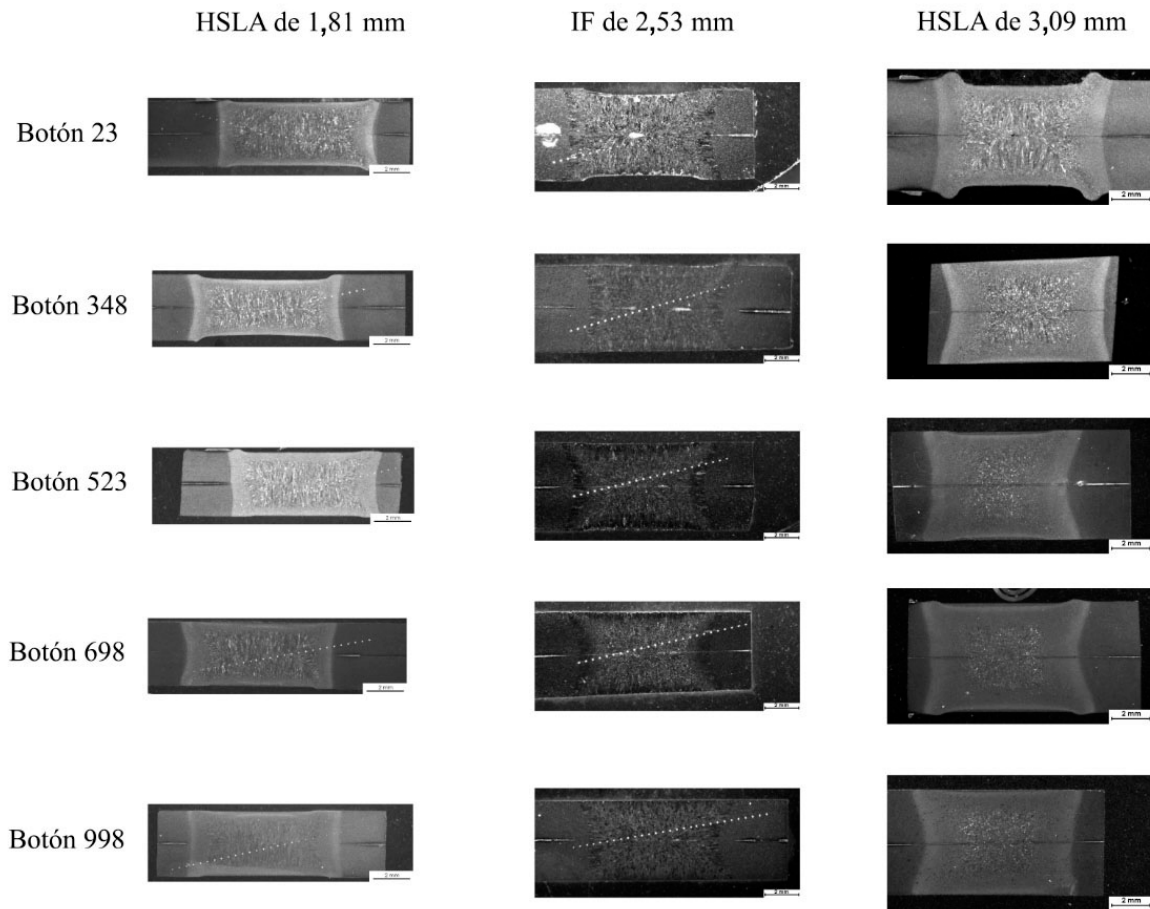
Macrografías de la sección transversal de los botones de soldadura.
